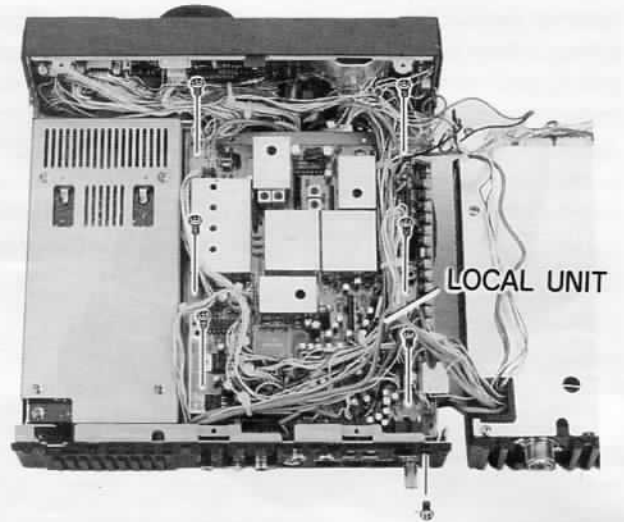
Mit diesen vier Schrauben ist die Oszillator-Platine befestigt
